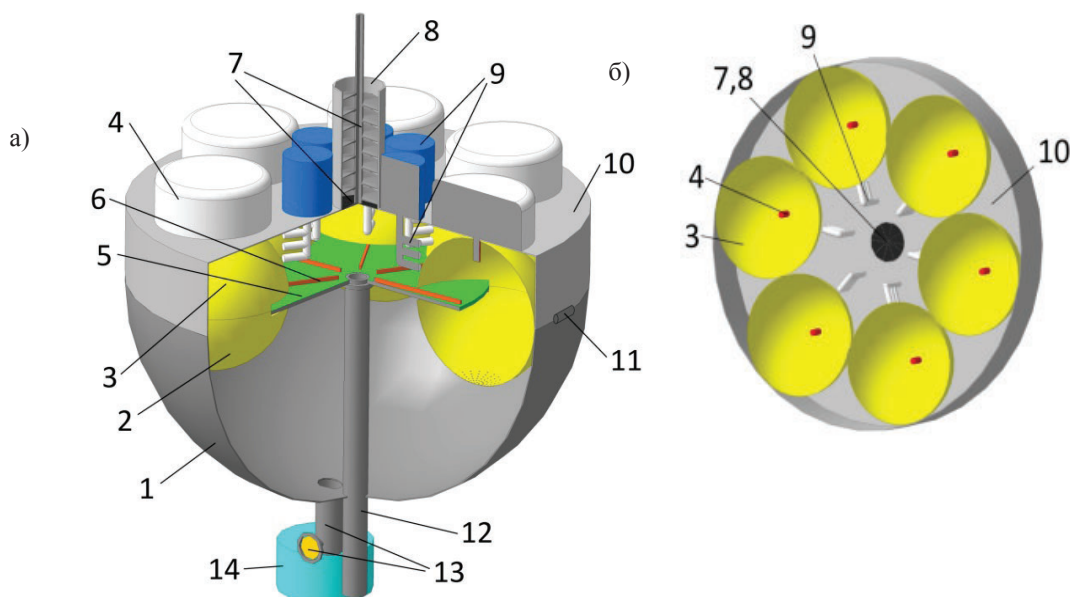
Сверхвысокочастотная установка со сферическими резонаторами для термообработки жиросодержащего сырья: а) общий вид в разрезе; б) узлы, прикреплённые на крышку экранирующего корпуса; 1 – экранирующий корпус; 2 – нижние перфорированные полусферы; 3 – верхние полусферы; 4 – сверхвысокочастотные генераторные блоки; 5 – диск из неферромагнитного материала; 6 – направляющие из неферромагнитного материала; 7 – измельчающий механизм (ножи, решётки, нагнетательный шнек); 8 – приёмный патрубок; 9 – источники энергии килогерцовой частоты с электрогазоразрядными лампами; 10 – крышка экранирующего корпуса; 11 – шарнирные петли; 12 – вал привода диска; 13 – сливной патрубок с вентилем; 14 – шестерёнчатый насос
